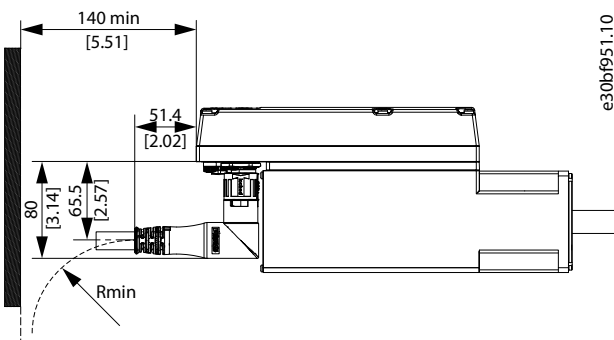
Mindestabstand für angewinkelten M23-Stecker
